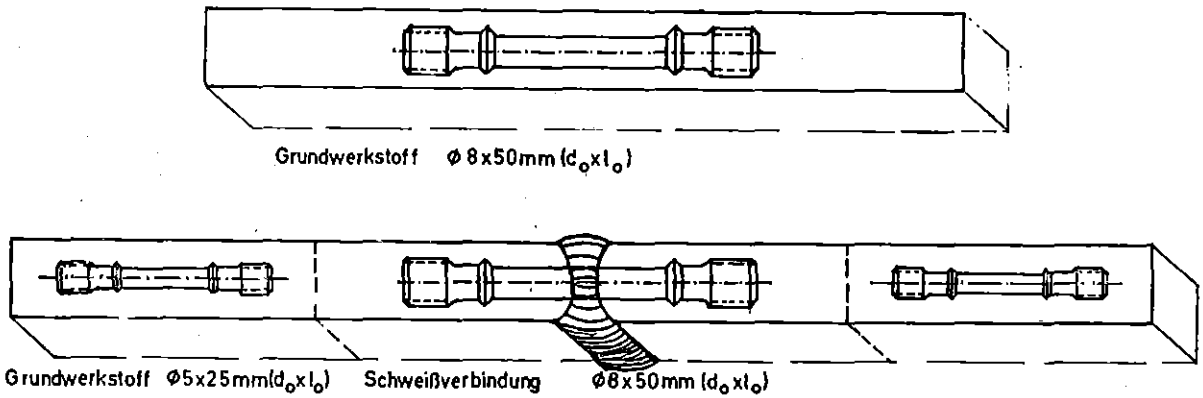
a : Probenlage in den Versuchsmaterialabschnitten, geschweißt und ungeschweißt
